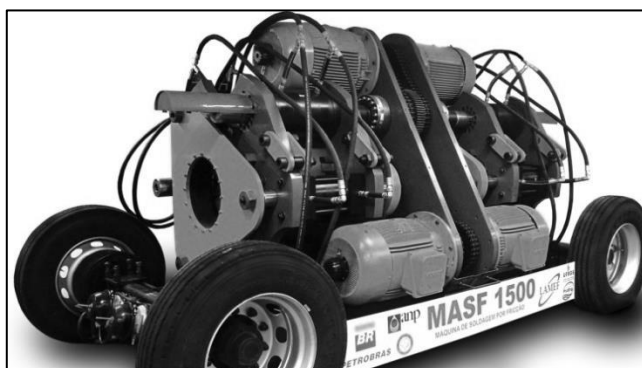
Máquina de Soldagem por Fricção (MASF 1500) projetada e desenvolvida pelo LAMEF.
